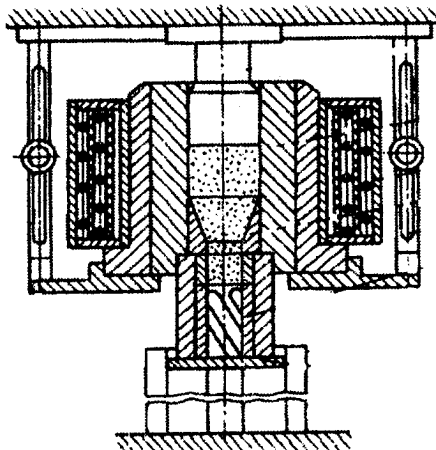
Схема пресування заготовок кінцевих інструментів з хвостовиками
